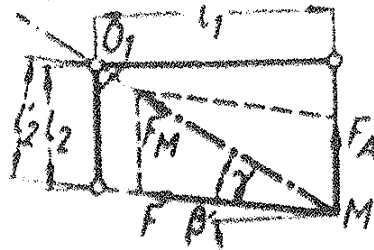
Çift pabuçlu fren sisteminde, fren kollarındaki kuvvetler [L-1].
